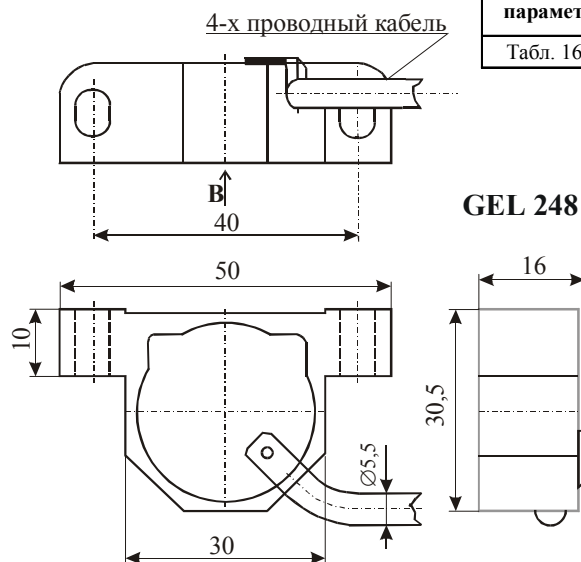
Внешний вид и габаритные размеры датчиков серии GEL 248
